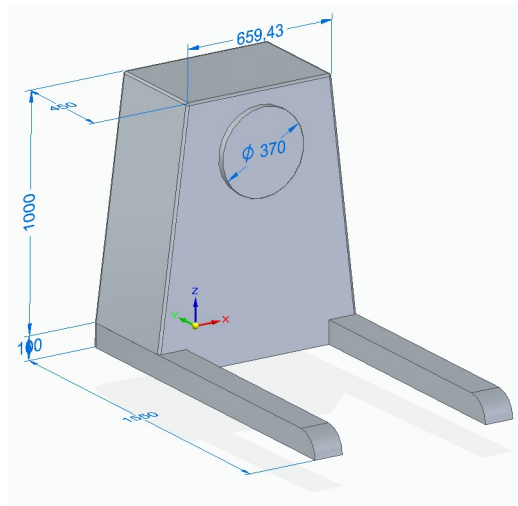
Manipulátor od firmy FÖRSTER.[5]
